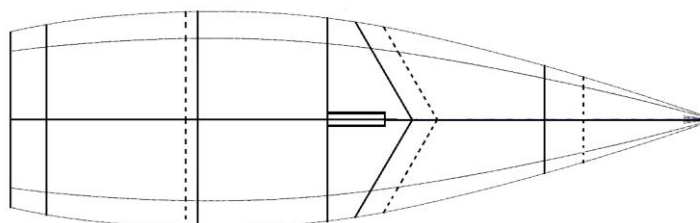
Illustrazione del posizionamento delle strutture interne. Le linee tratteggiate corrispondono alla posizione delle strutture interne di Ate mentre le linee piene a quelle di Athena
